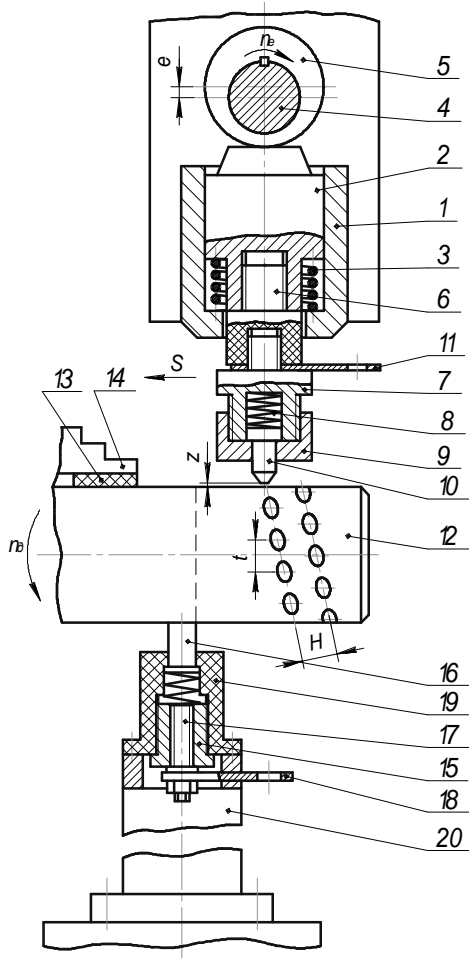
Установка деталі і пристрій для електроконтактної дискретної обробки зовнішньої поверхні
